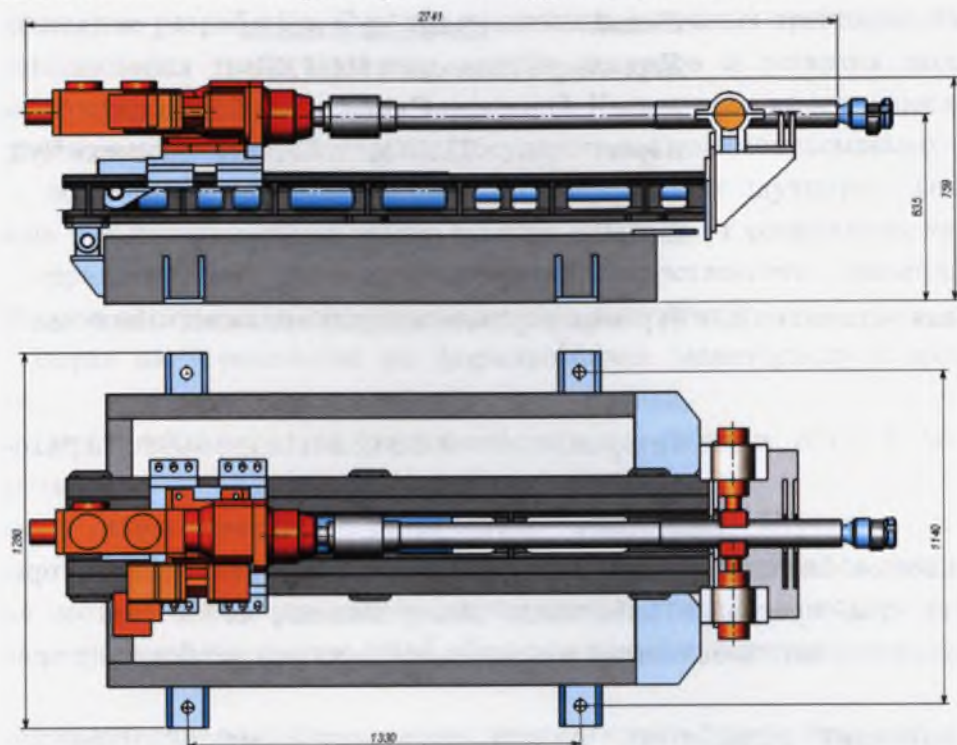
Буровая установка «Импульс 796»: 1- рама; 2- проушина для крепления анкера; 3- салазка; 4- вращательно-ударный механизм; 5- вертлюг для подачи воздуха; 6- буровая штанга; 7- направляющий; 9- коронка; 10- люнет зажим; 11- гидроцилиндр подачи бурового става; 12- гидромотор вращателя.
